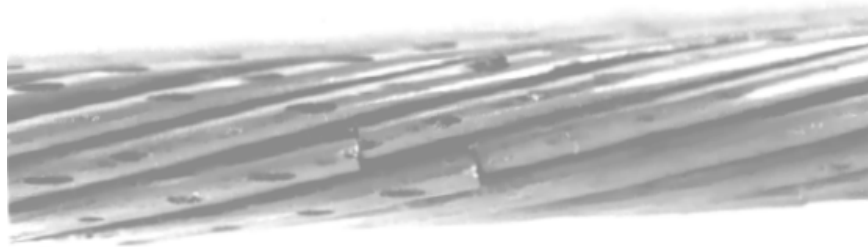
Desgaste por fretting en conductor. ([IEEE 1368-2006](#))
